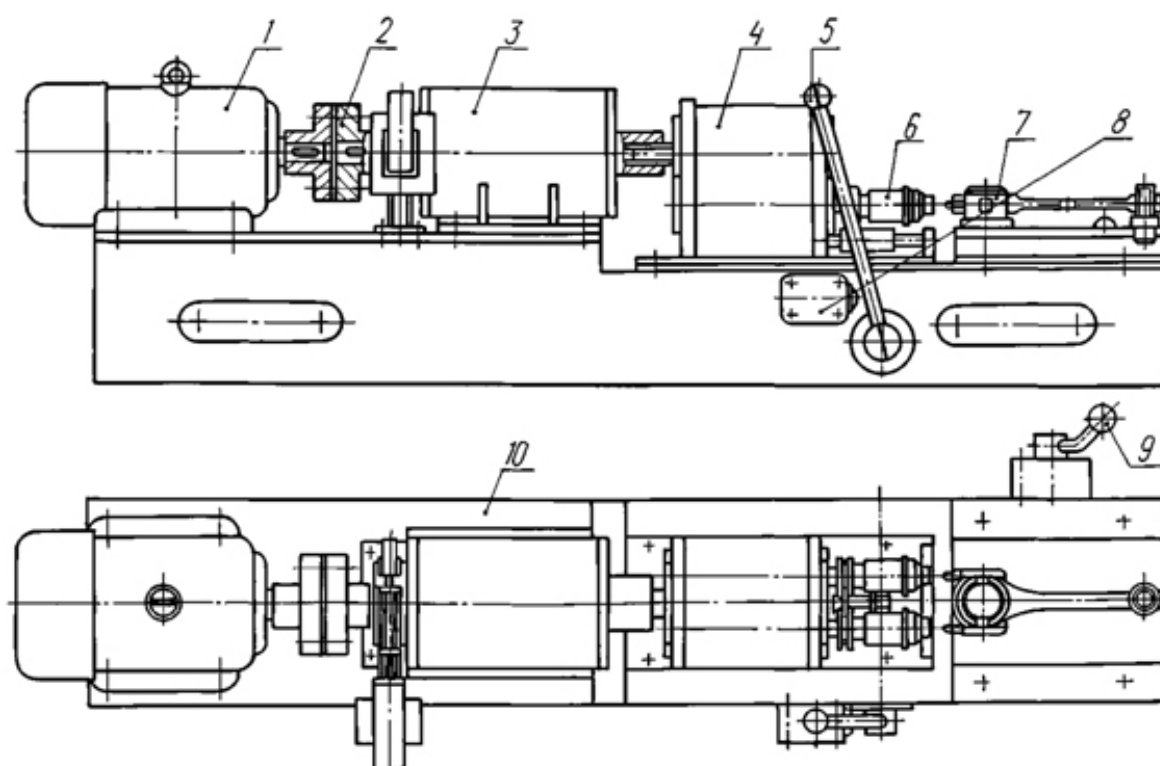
Схема гайковерта для шатуна: 1 – электродвигатель; 2 – муфта; 3 – редуктор; 4 – делитель момента; 5 и 9 – рукоятки; 6 – ключ; 7 – опорный механизм; 8 – конечный выключатель; 10 – основание
